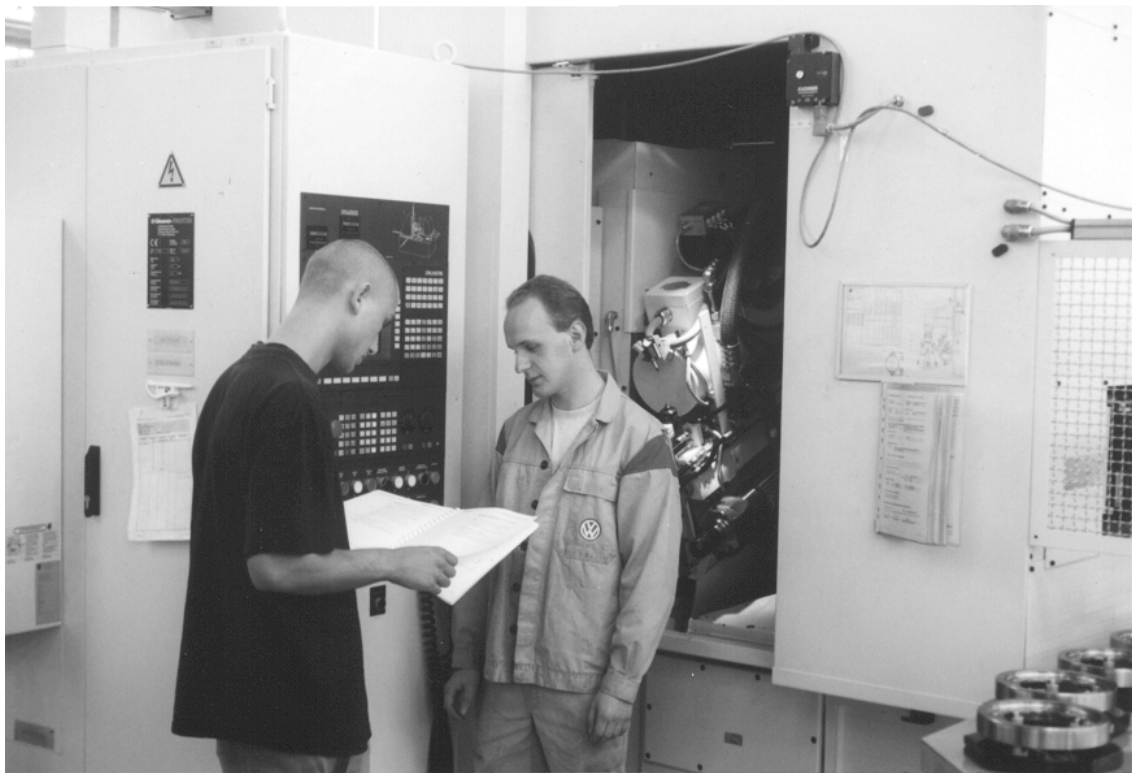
Azubildende studieren Maschinenunterlagen zwecks Werkzeugwechsels an einer Fräsmaschine für Verzahnung.
